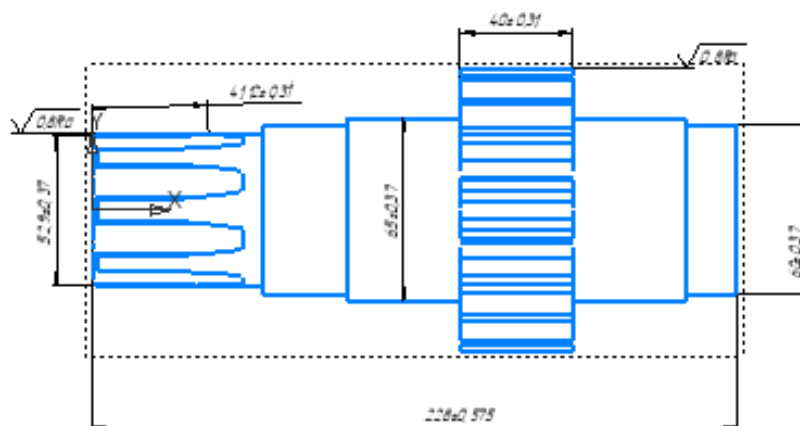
Чертеж детали «Шлицевой вал-шестерня»
